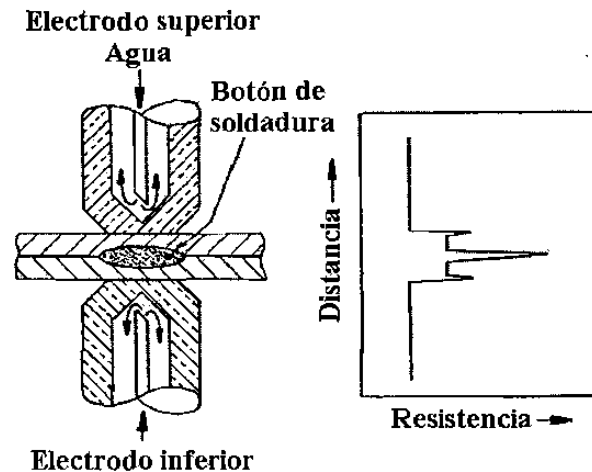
Ilustración esquemática del proceso de soldadura por puntos⁽⁴²⁾.
